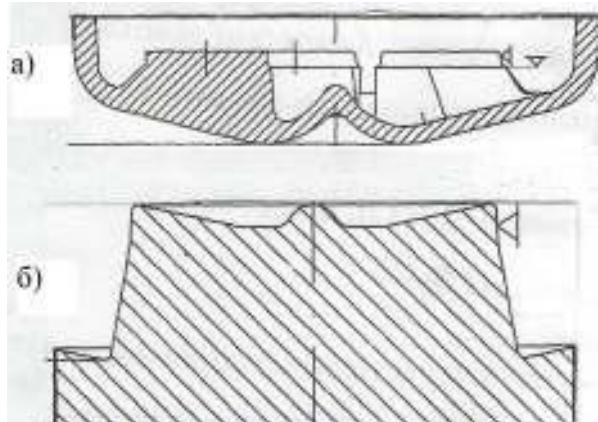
Штампованные детали наконечника фурмы: а) - медный венец; б) - стальной корпус
